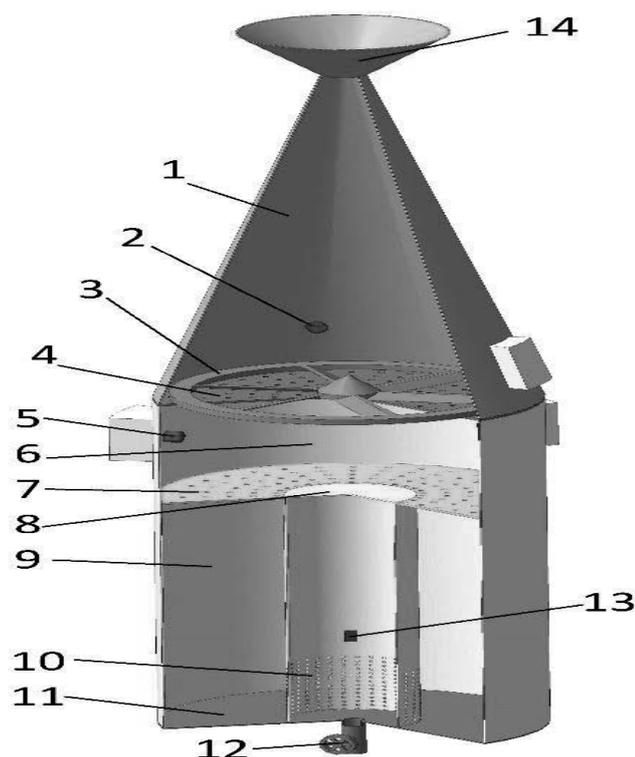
СВЧ установка для размораживания и разогрева коровьего молозива:
